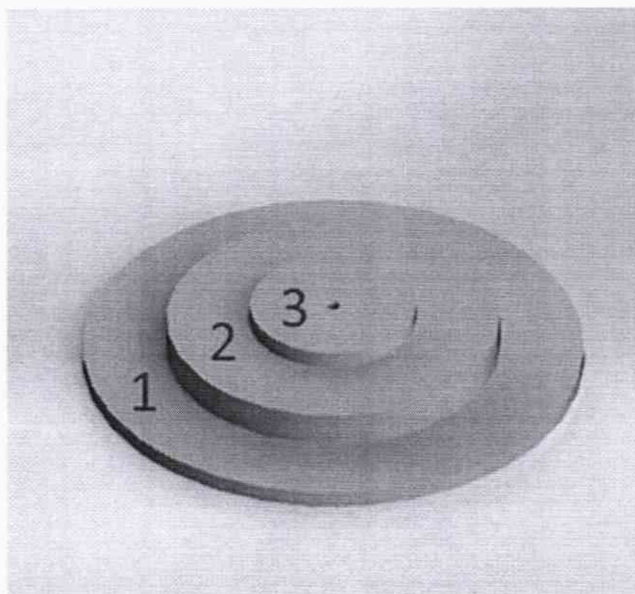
ВАПМ.311В.051.02 с нумерацией поверхностей
